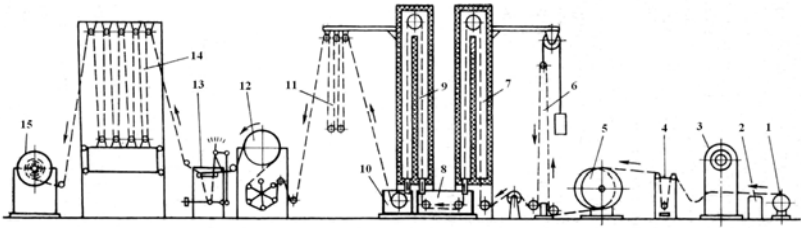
Автоматична лінія виготовлення та термічної обробки гачкових деталей
